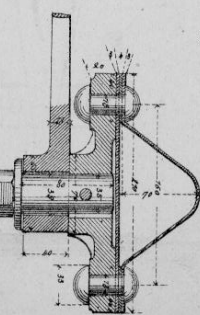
Elevation du poteau de manœuvre à 0,04 p^r 1^m
